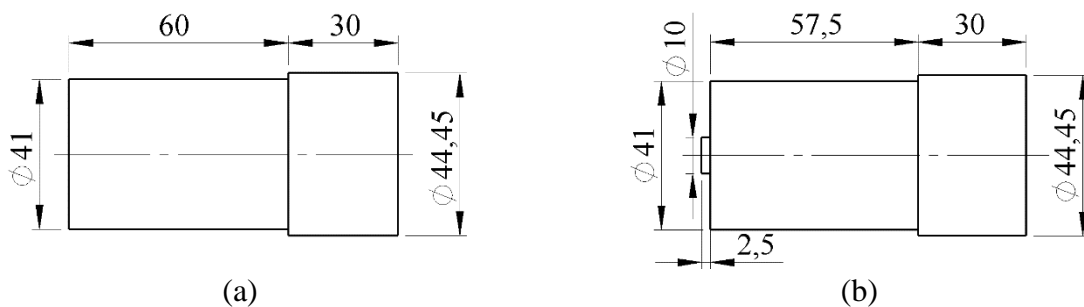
Corpo de prova referente à Etapa 2: (a) dimensões iniciais; (b) representação após faceamento com largura de corte 2,5 mm (dimensões em mm).
